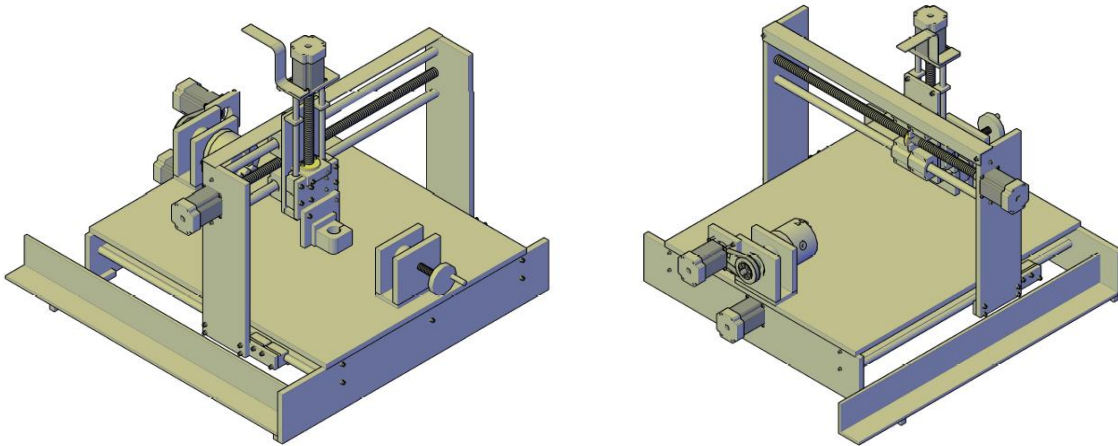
Ensamblaje de la maquina fresadora CNC [Fuente propia].
